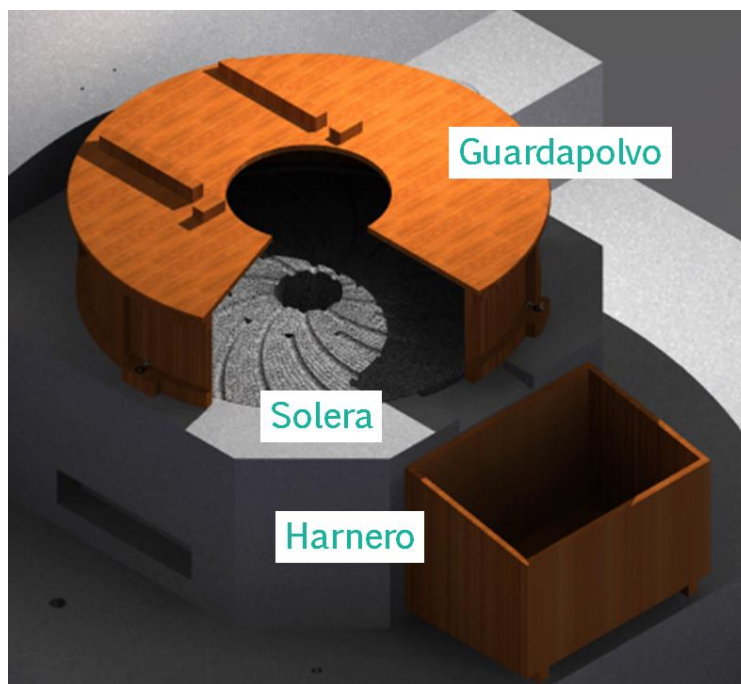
Vista general del conjunto solera, guardapolvo y harnero.
